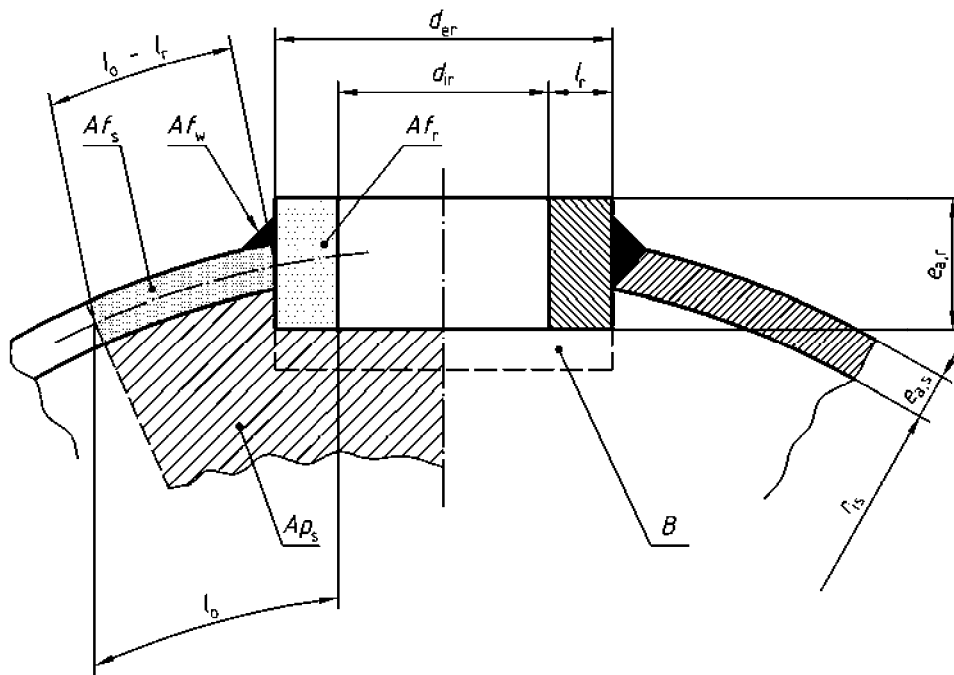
Envoltente esférica o fondo cóncavo con abertura aislada y anillo de refuerzo con brida interna ciega B
